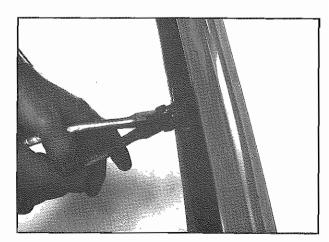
Guarnizione sul bordo del canale Gasket on the groove edge
